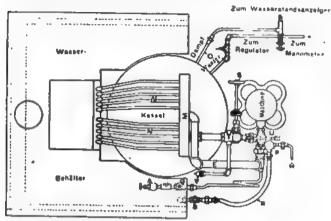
Grundriss der Kessel- und Maschinen-Anordnung.
